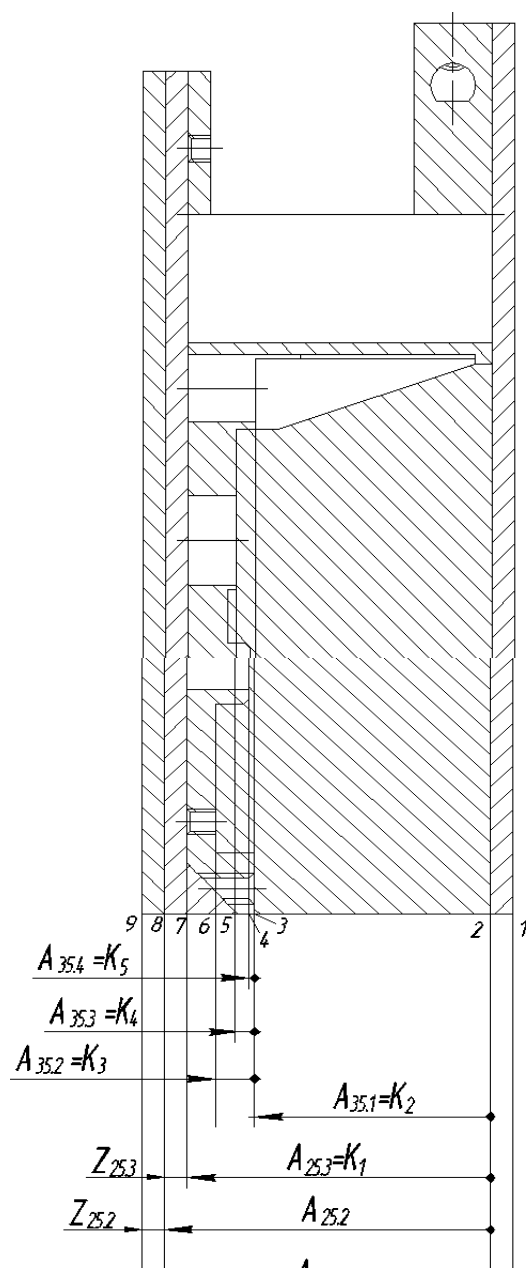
Комплексная схема обработки детали «Фланец»
